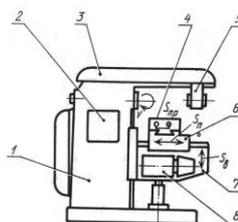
Горизонтально-фрезерный станок: 1 – станина; 2 – коробка скоростей; 3 – хобот; 4 – стол; 5 – подвеска; 6 – салазки; 7 – консоль; 8 – коробка подачи.
